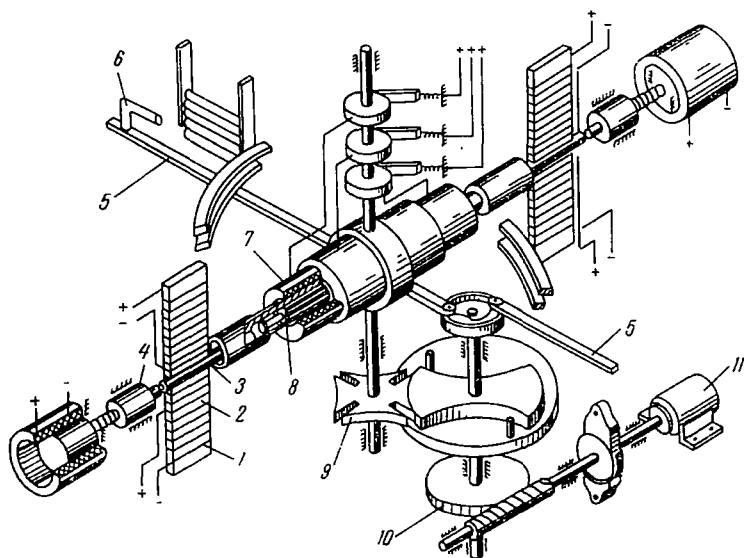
Схема станка для магнитно-абразивной обработки по [2]
